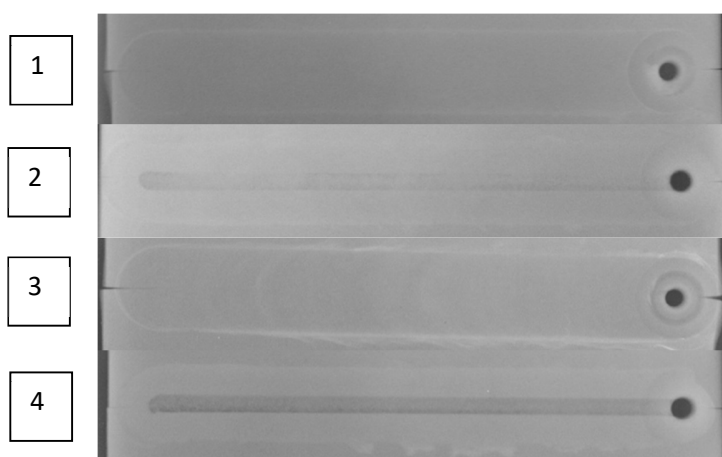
Radiografías de cordones de soldadura obtenidos mediante FSW. De arriba abajo 90 mm/min – 1085 RPM, 127 mm/min – 1400 RPM, 45 mm/min – 1085 RPM y 187 mm/min – 1400 RPM.
